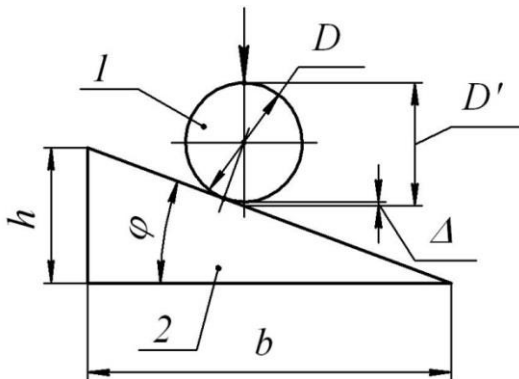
Базування по циліндричній поверхні деталі
